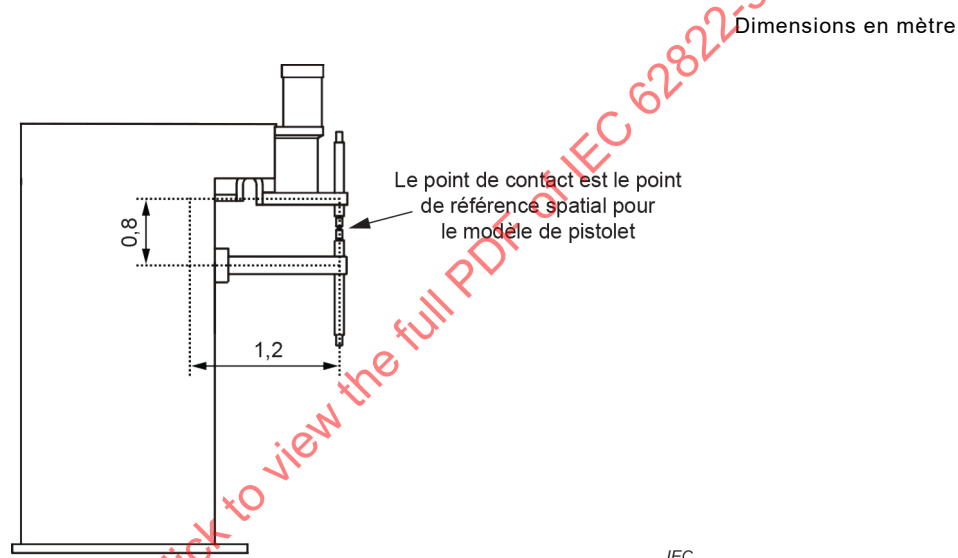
Géométrie du pistolet de soudage par point fixe
